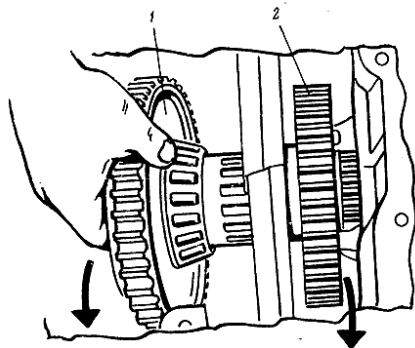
Снятие вторичного вала КПП: 1 — вторичный вал; 2 — ведомая шестерня II ступени редуктора
